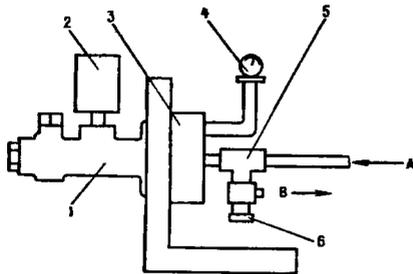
Схема проверки состояния заднего уплотнительного кольца на герметичность: 1 - главный цилиндр; 2 - сосуд; 3 - переходник с уплотнителем; 4 - манометр; 5 - тройник; 6 - регулировочный винт; А - воздух от компрессора; В - выпуск воздуха
